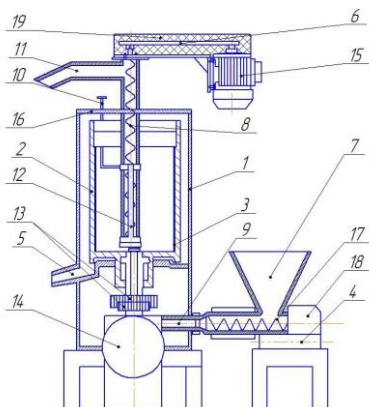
Фильтрующая центрифуга с вертикально расположенным фильтрующим барабаном. 1-корпус; 2-фильтрующий барабан; 3-сетка; 4-питатель; 5- патрубок выгрузки жидкой фракции; 6- клиноременная передача; 7- бункер; 8-шнек разгрузочного устройства; 9-трубопровод; 10- рычаг; 11-патрубок разгрузочный; 12-подвижный скребок; 13-шестеренчатая передача; 14-двигатель центрифуги; 15- двигатель разгрузочного устройства; 16- крышка центрифуги; 17-шнек разгрузочного устройства; 18-мотор-редуктор привода питателя; 19- защитное ограждение клиноременной передачи;
